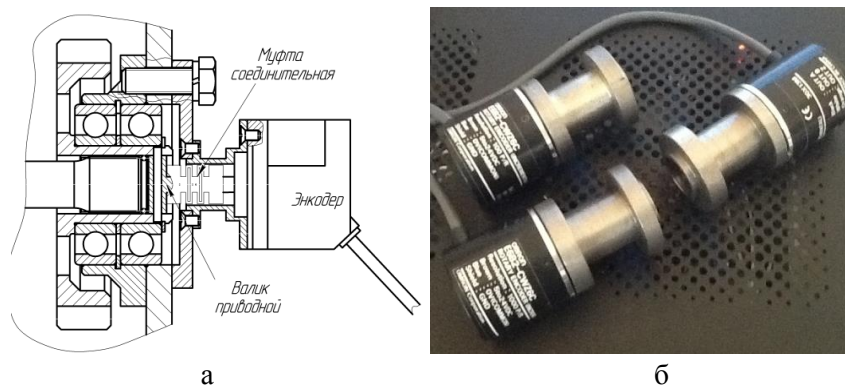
Эскиз установки и внешний вид энкодера Omron
